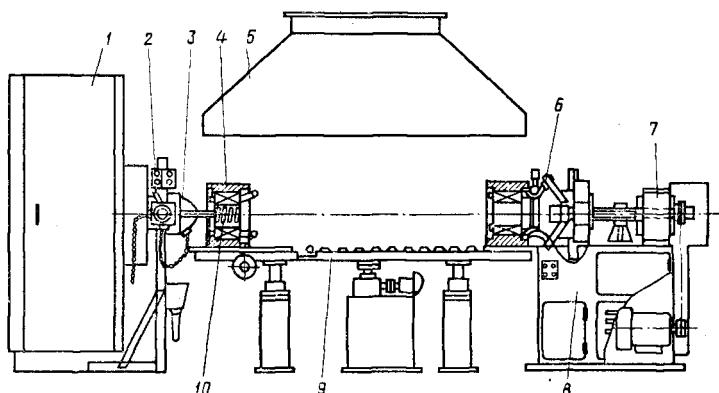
Схема высокочастотной установки для разогрева и извлечения обмотки статора
